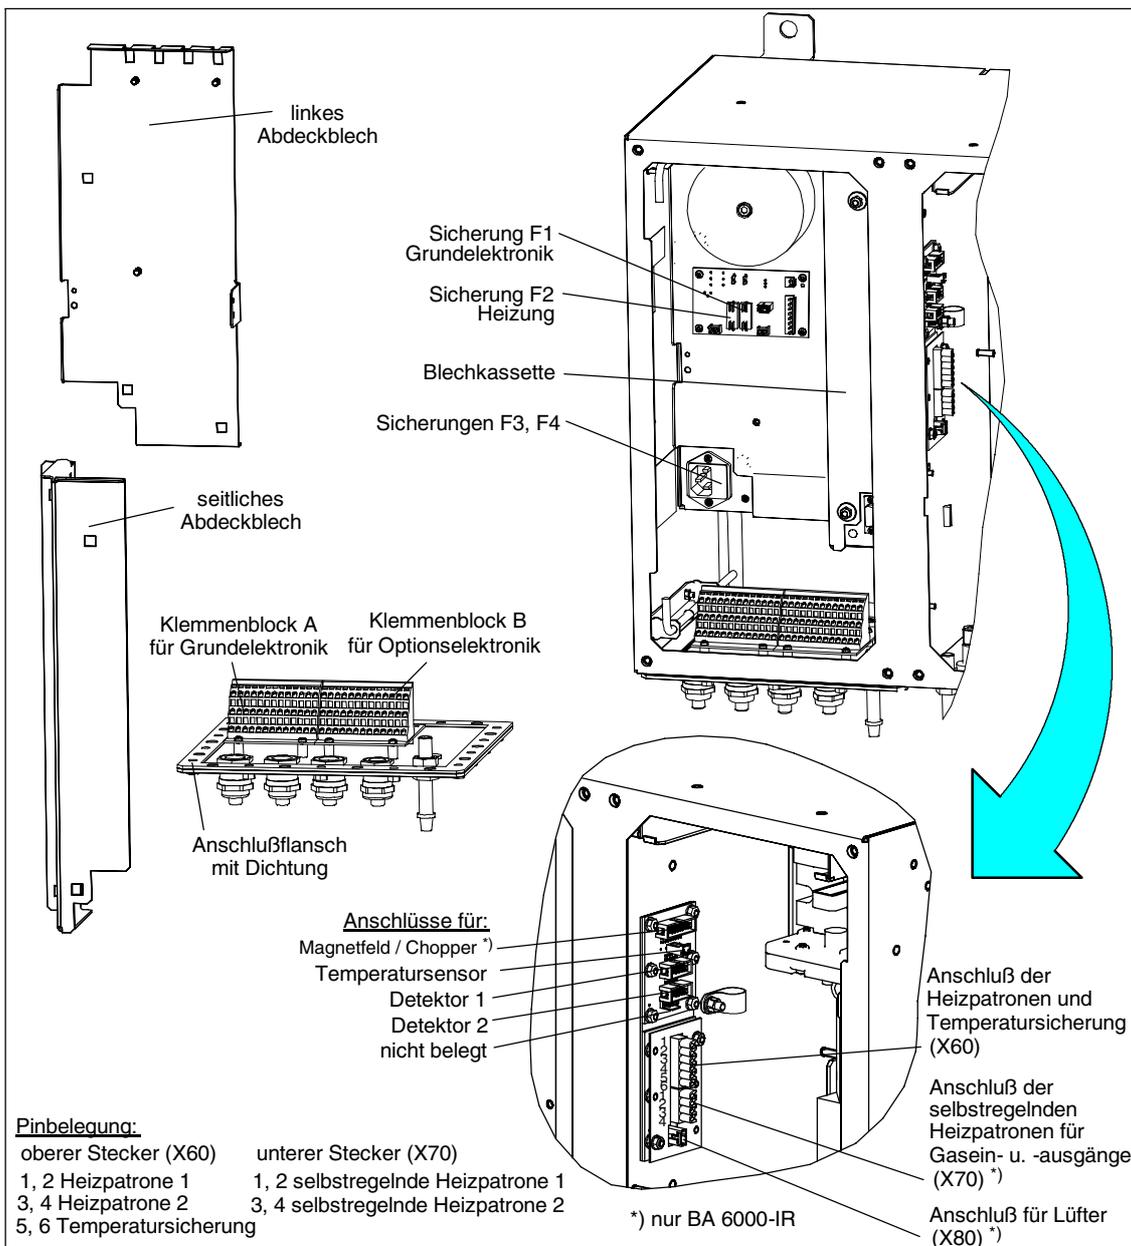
BA 6000 Feldgeräte (beheizte Ausführung)
